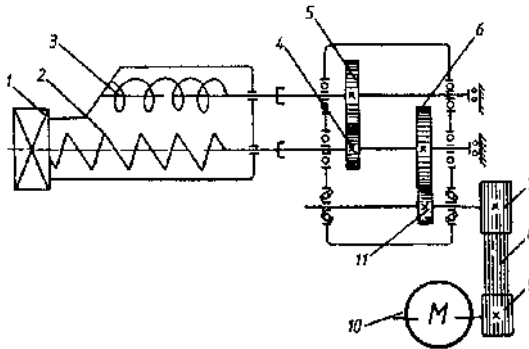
Кінематична схема вовчка МП-1-160: 1 - ріжучий механізм; 2, 3 - живильний, подавальний шнеки; 4, 11 - шестірни; 5, 6 - зубчасті колеса; 7, 9 - шківі; 8 - клинові паси; 10 - електродвигун
